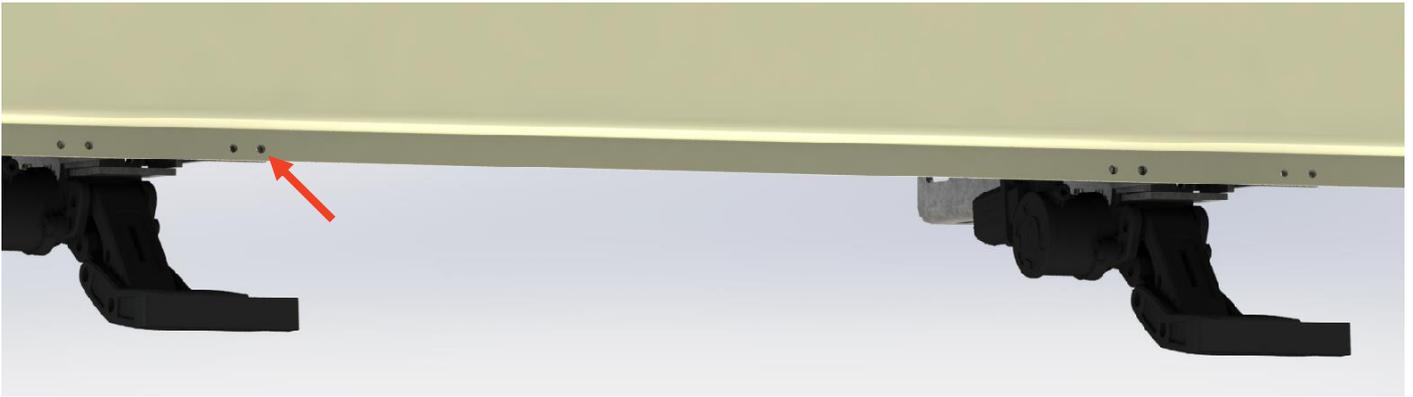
Bohrungen 8x $\varnothing 6,5\text{mm}$ am Schweller
